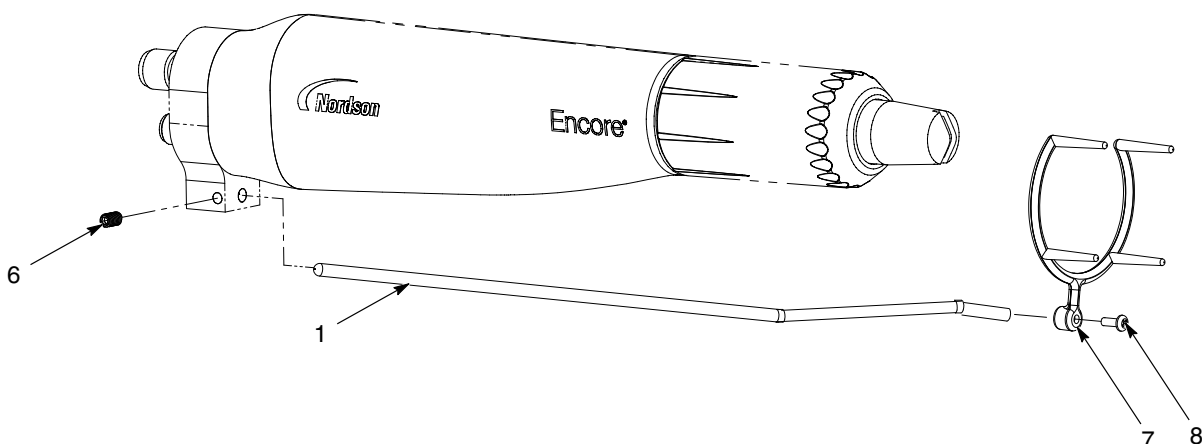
Installation du collecteur d'ions – Pistolet à fixation sur barre
